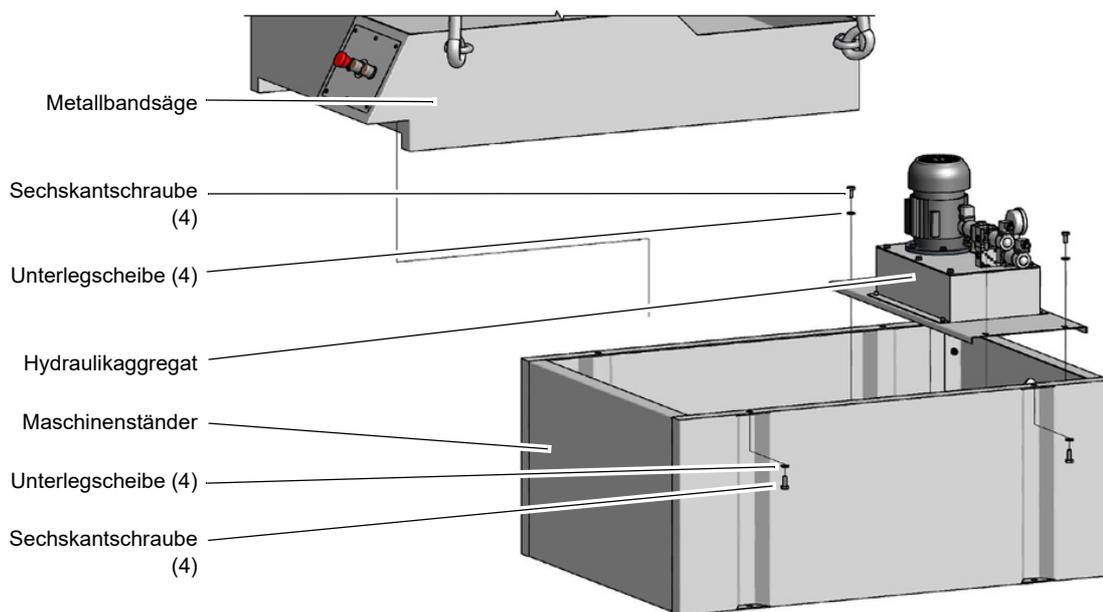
Montageskizze des Hydraulikaggregates und der Metallbandsäge
